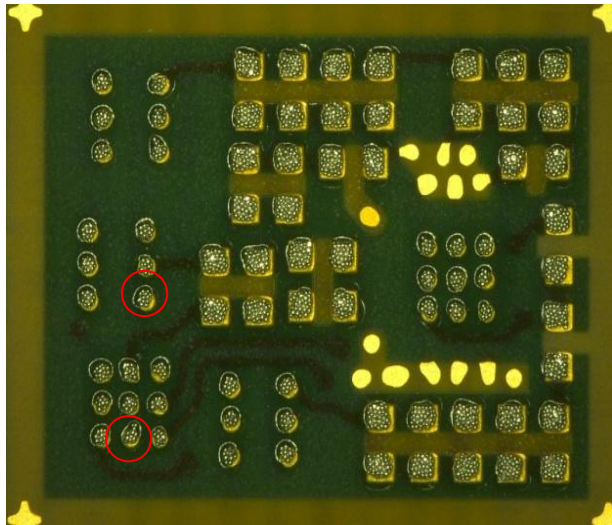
Impresión de soldadura de pasta a 100 micrones abertura cuadrada
